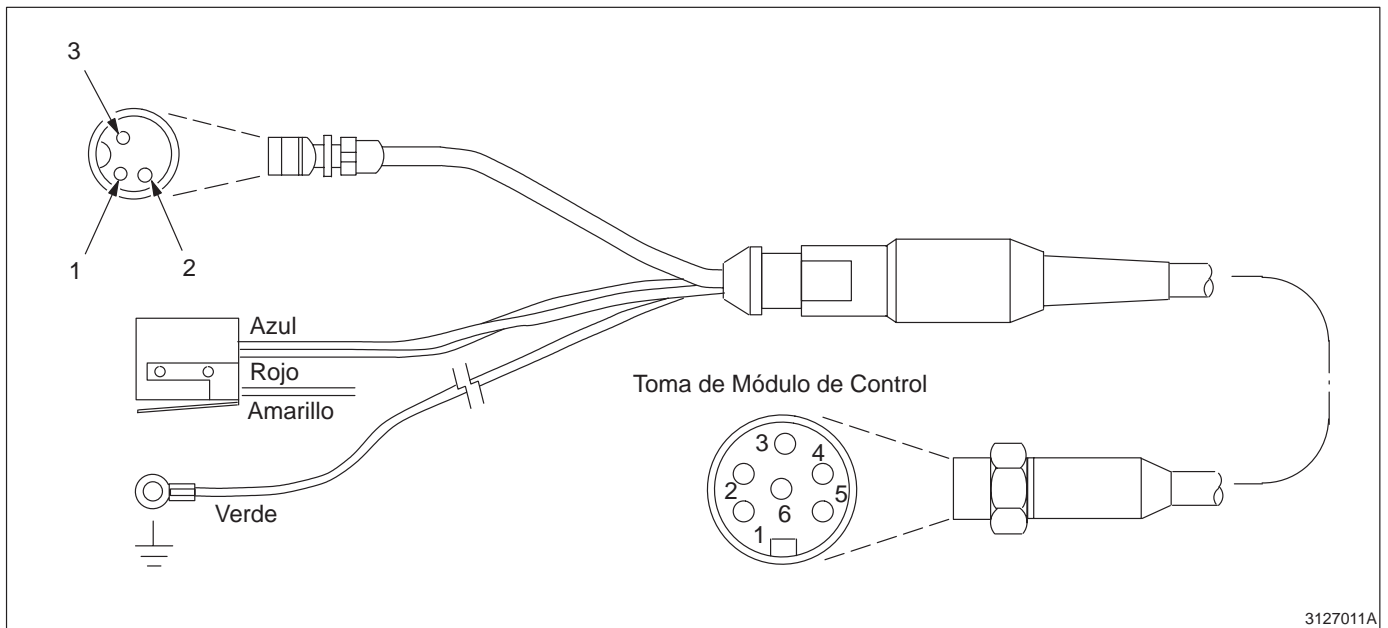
Comprobación de la continuidad del cable de la pistola
